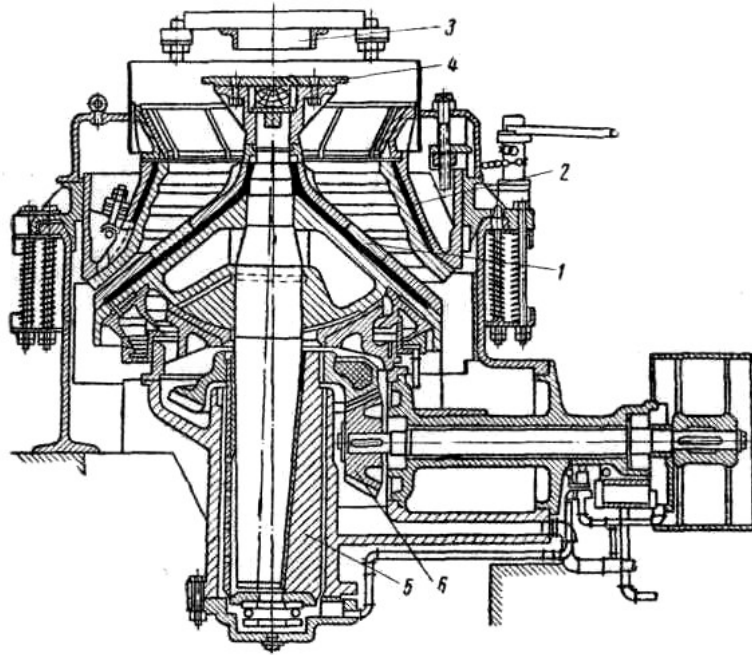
Конусная дробилка для среднего дробления: 1 – подвижный конус; 2 – неподвижный конус; 3 – загрузочная воронка 4 – тарельчатый питатель 5 – эксцентриковый стакан; 6 – зубчатая передача
